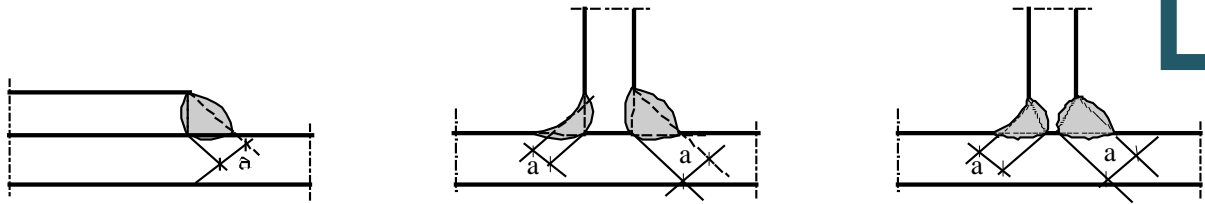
Exemples d'épaisseurs "a" de quelques cordons de soudures.
